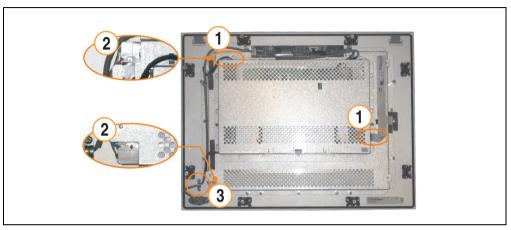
Automation Panel 15" - Schrauben und Stecker lösen
